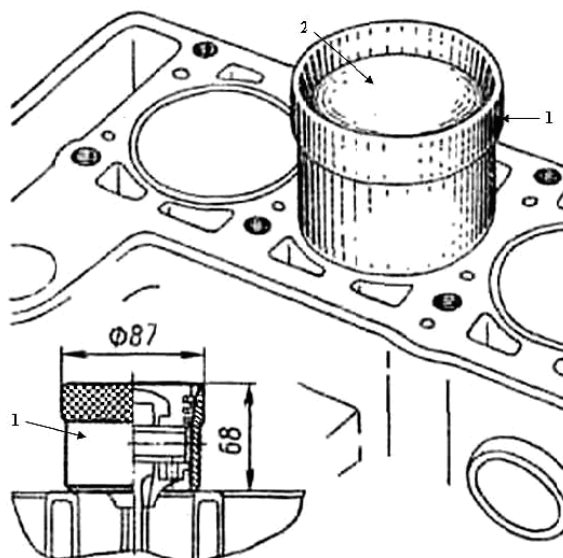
Установка поршня с поршневыми кольцами и шатуном в цилиндр двигателя при помощи оправки – обжима для колец:
